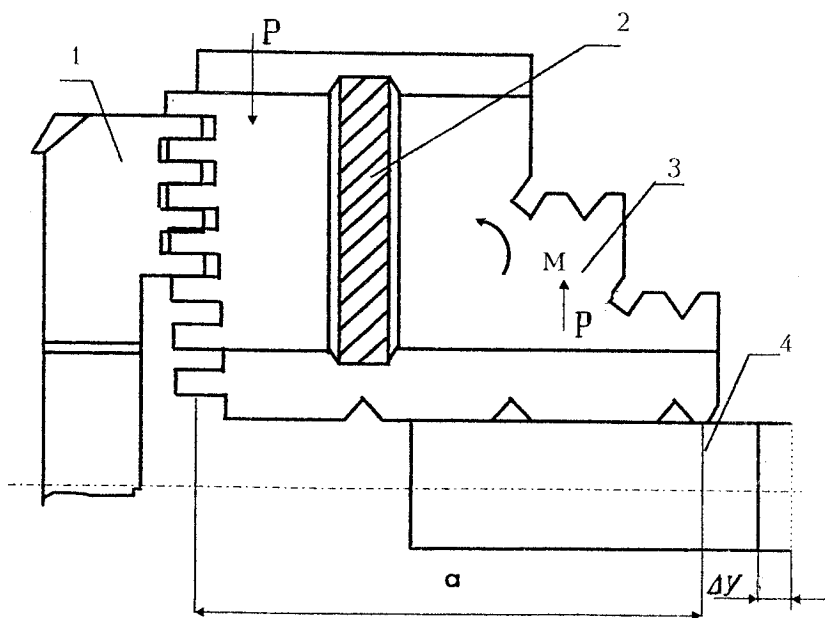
Схема закріплення заготовки у токарному патроні
